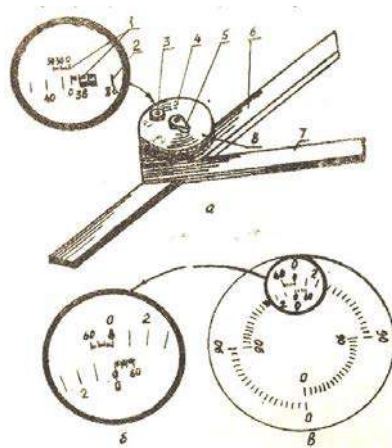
Оптический угломер и его шкала: а) оптический угломер; б) видимая перед глазами шкала; в) градусная и минутная шкала. 1-минутная, 2-градусная шкала, 3 – лупа, 4 - корпус, 5 – зажимной рычаг, 6 – подвижная линейка, 7 –неподвижная линейка, 8-кольцо.
